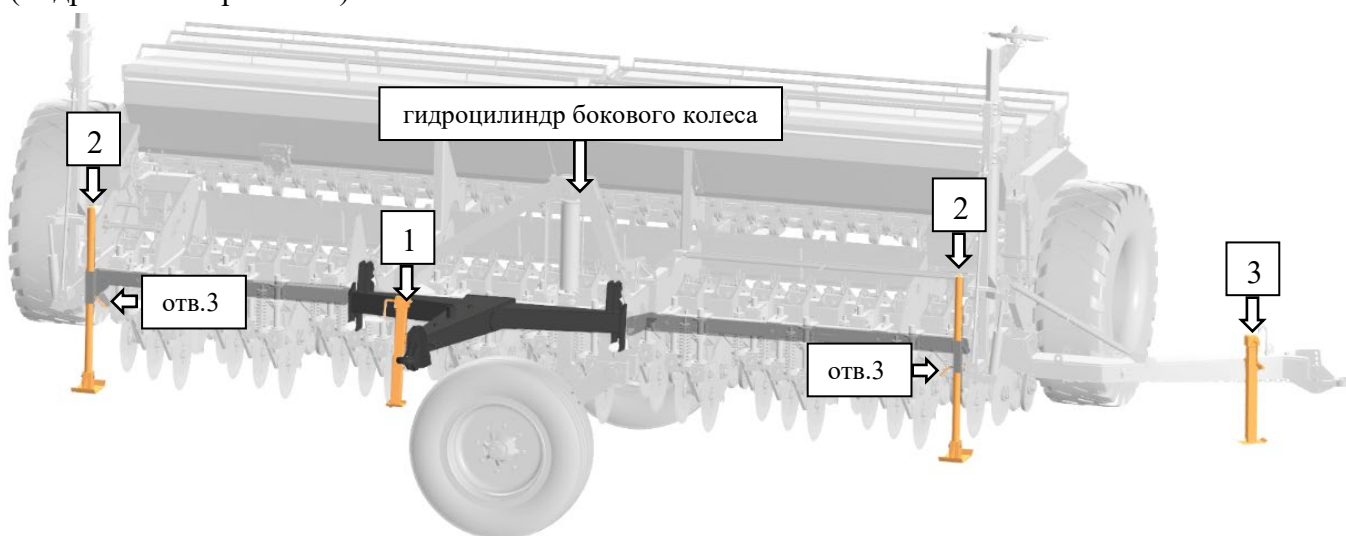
Подготовка к установке сеялки на опорно-приводные колёса
